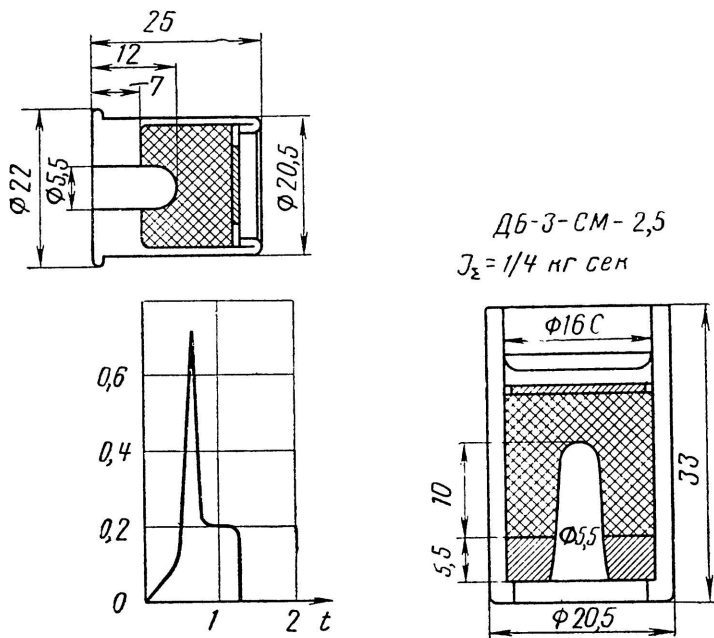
Модельный ракетный двигатель ДБ-3-СМ-2,5.
